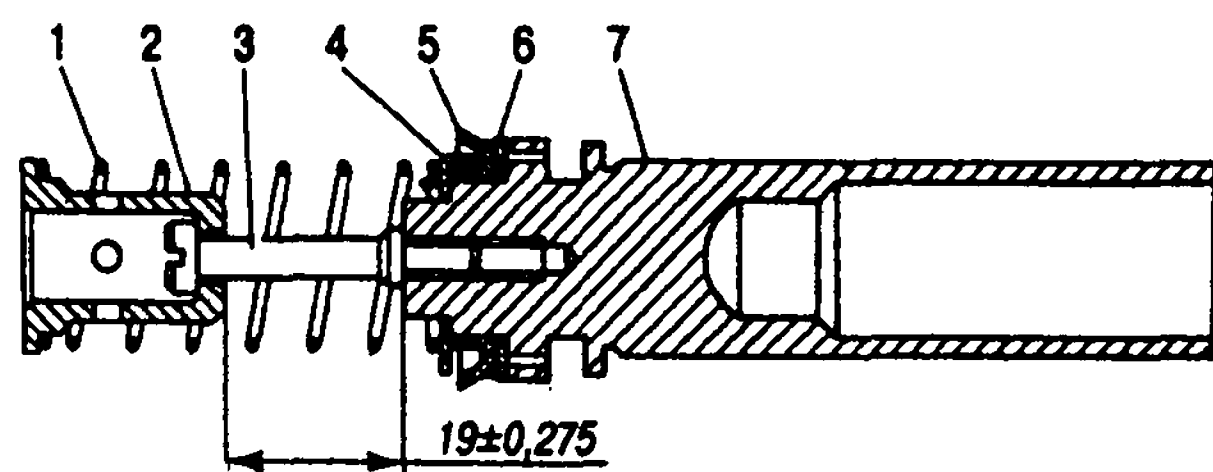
Первичный поршень главного цилиндра: 1 - пружина; 2 - держатель пружины; 3 - винт; 4 - упорная шайба; 5 - манжета; 6 - шайба; 7 - поршень
